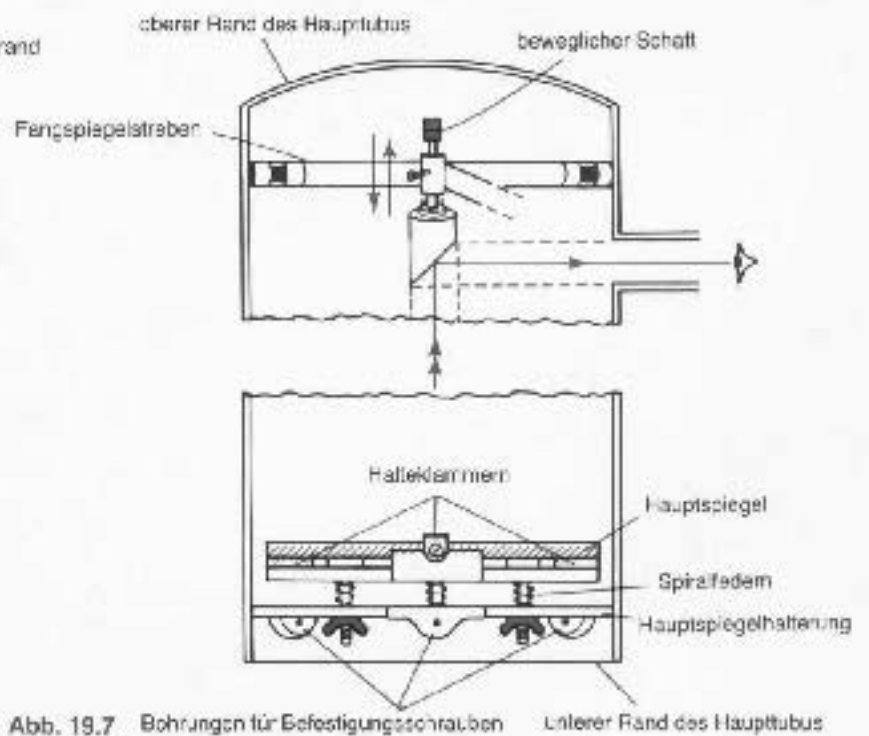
Bohrungen für Befestigungsschrauben Unterer Rand des Haupttubus
